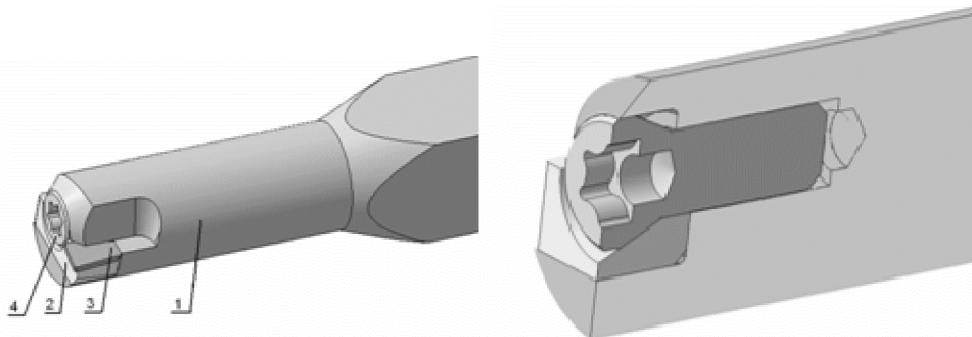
механическое крепление режущих пластин: 1 – державка инструмента; 2 – твердосплавная пластина; 3 – СТМ на основе кубического нитрида бора; 4 – винт
